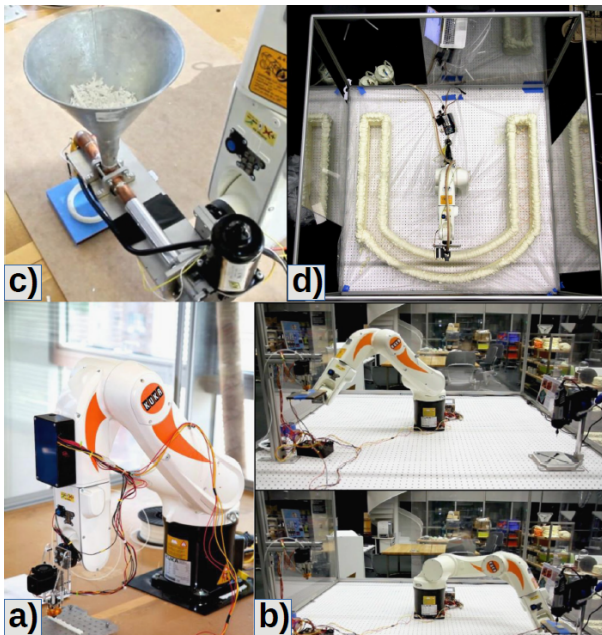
(a) Impresión 3D con cabezal tradicional, (b) Plataforma para manufactura aditiva y sustractiva, (c) Impresión 3D a través del reciclaje de polietileno de alta densidad, (d) Impresión 3D con deposición por espuma de etano [3].
